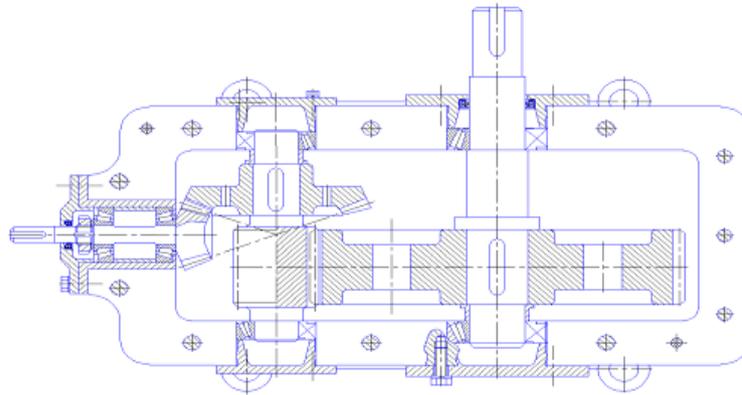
Редуктор двухступенчатый коническо-цилиндрический
